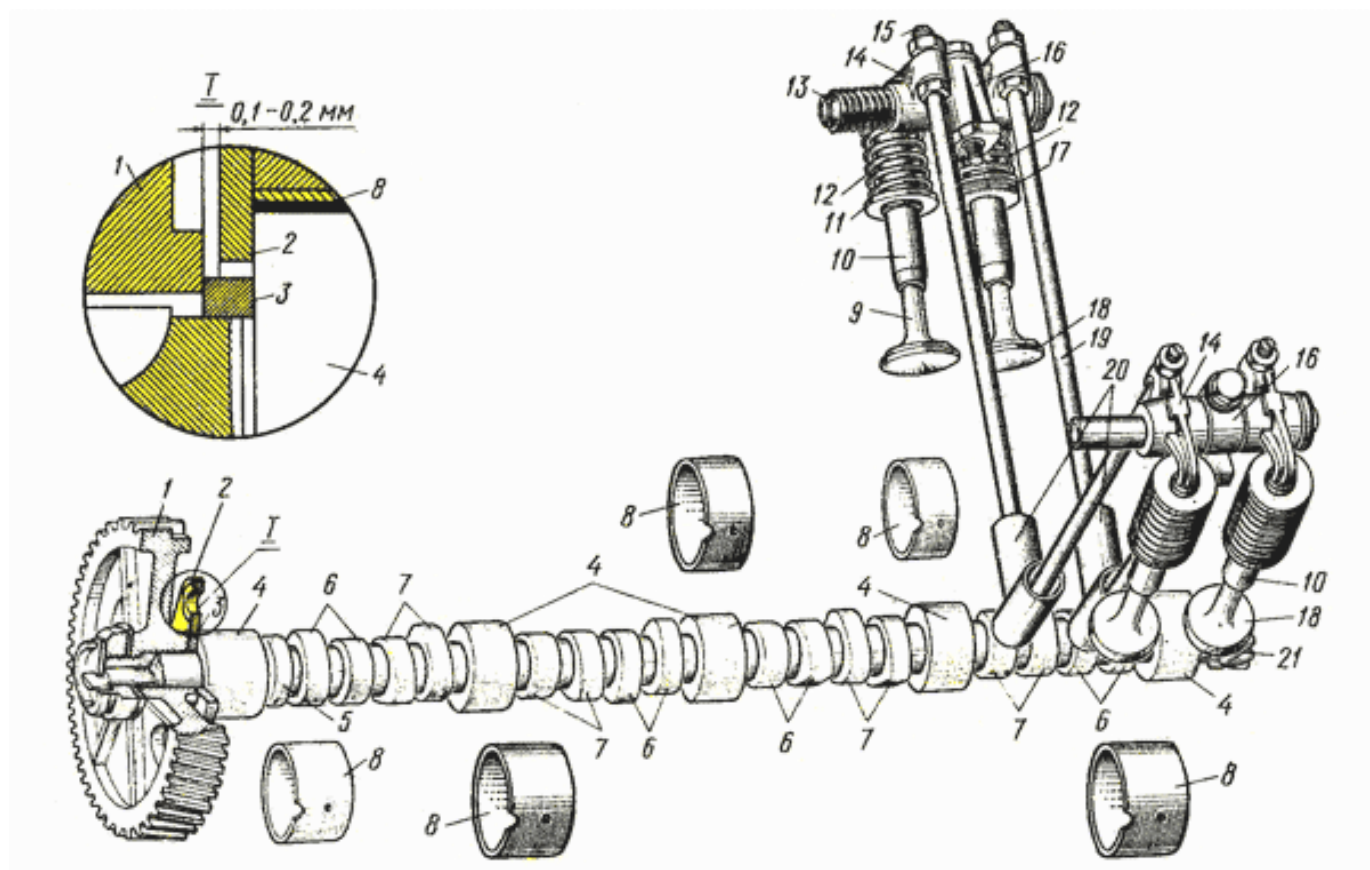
Механізм газорозподілу: 1 – шестерня розподільного валу; 2 – упорний фланець; 3 – розпірне кільце; 4 – опорні шийки; 5 – ексцентрик приводу паливного насоса; 6 – кулачки випускних клапанів; 7 – кулачки впускних клапанів; 8 – втулки; 9 – впускний клапан; 10 – направляюча втулка; 11 – упорна шайба; 12 – пружина; 13 – ось коромисел; 14 – коромисло; 15 – регулювальний гвинт; 16 – стійка вісі коромисел; 17 – механізм повороту випускного клапана; 18 – випускний клапан; 19 – штанга; 20 – штовхачі; 21 – шестерня приводу масляного насоса і переривника-розподільника.
